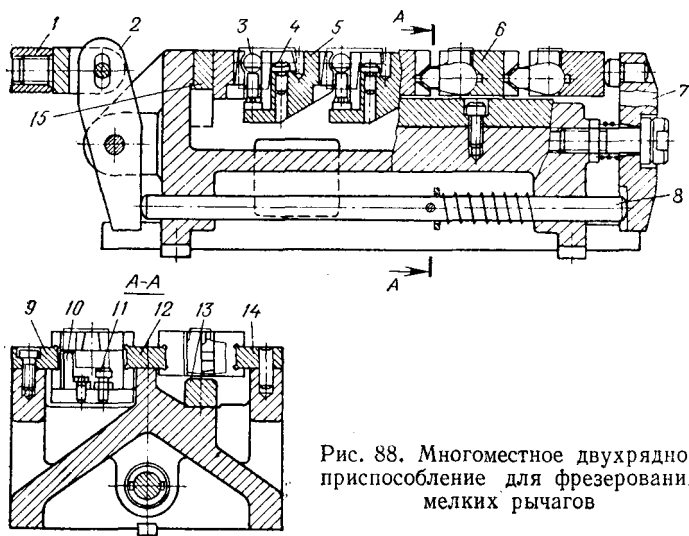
Многоместное двухрядное приспособление для фрезерования мелких рычагов
